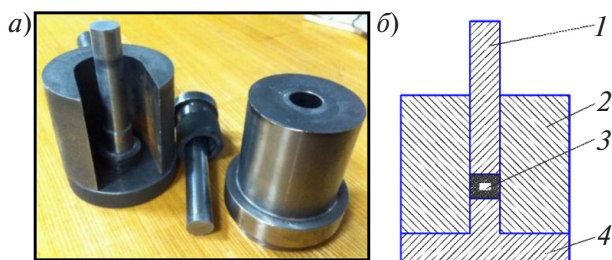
Общий вид (а) и схема (б) пресс-оснастки для прессования металлических порошков: 1 – верхний пуансон; 2 – матрица; 3 – порошок; 4 – нижний пуансон
